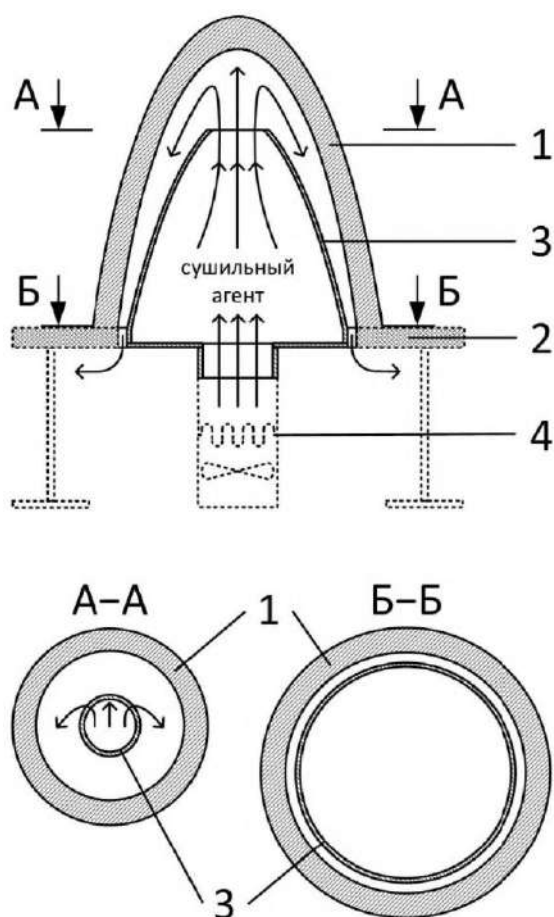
Схема предложенного воздуховода: 1 – керамическая заготовка; 2 – платформа; 3 – воздуховод; 4 – тепловентильатор.
